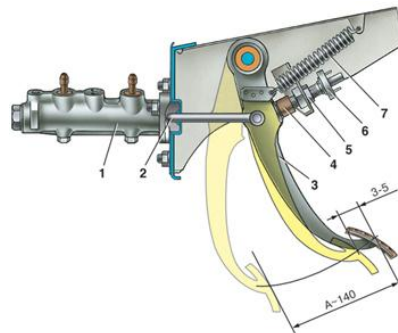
Регулировка свободного хода педали тормоза: 1 – главный цилиндр; 2 – толкатель; 3 – педаль тормоза; 4 – буфер выключателя стоп-сигнала; 5 – гайка выключателя; 6 – выключатель стоп-сигнала; 7 – оттяжная пружина педали
